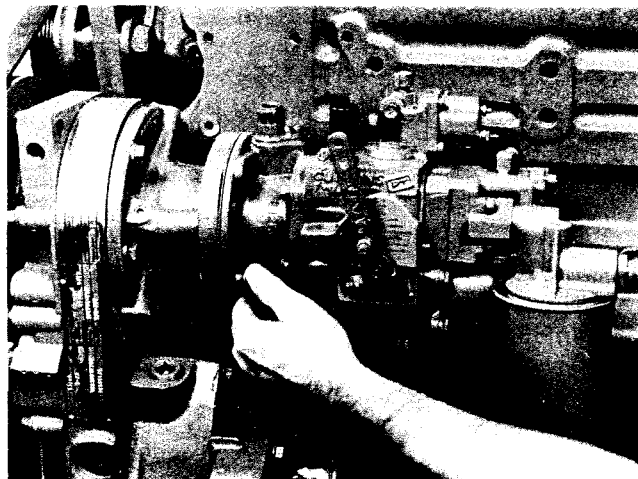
, (N114278). Instalación de la bomba de combustible.
